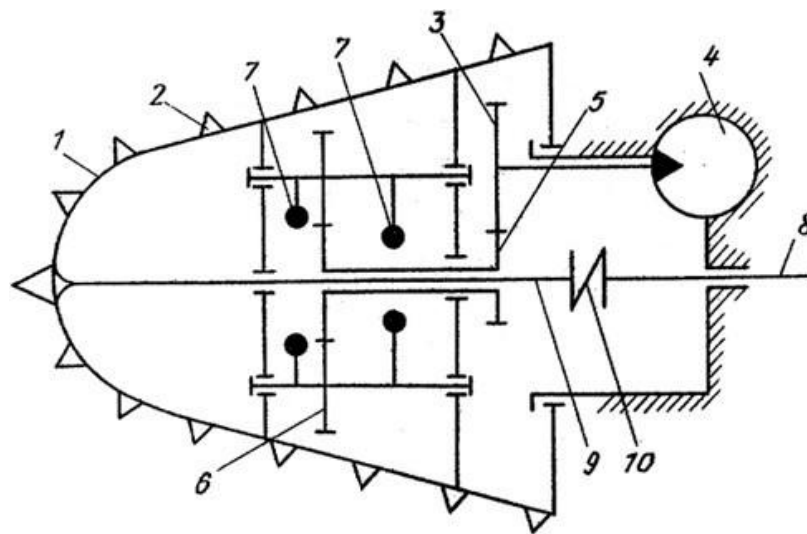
Виброактивный исполнительный орган: 1 – коронка; 2 – резцы; 3 – зубчатое колесо; 4 – гидродвигатель; 5 – блок-шестерня; 6 – сателлиты; 7 – неуравновешенные массы; 8 – приводной вал; 9 – вал коронки; 10 – гаситель колебаний
